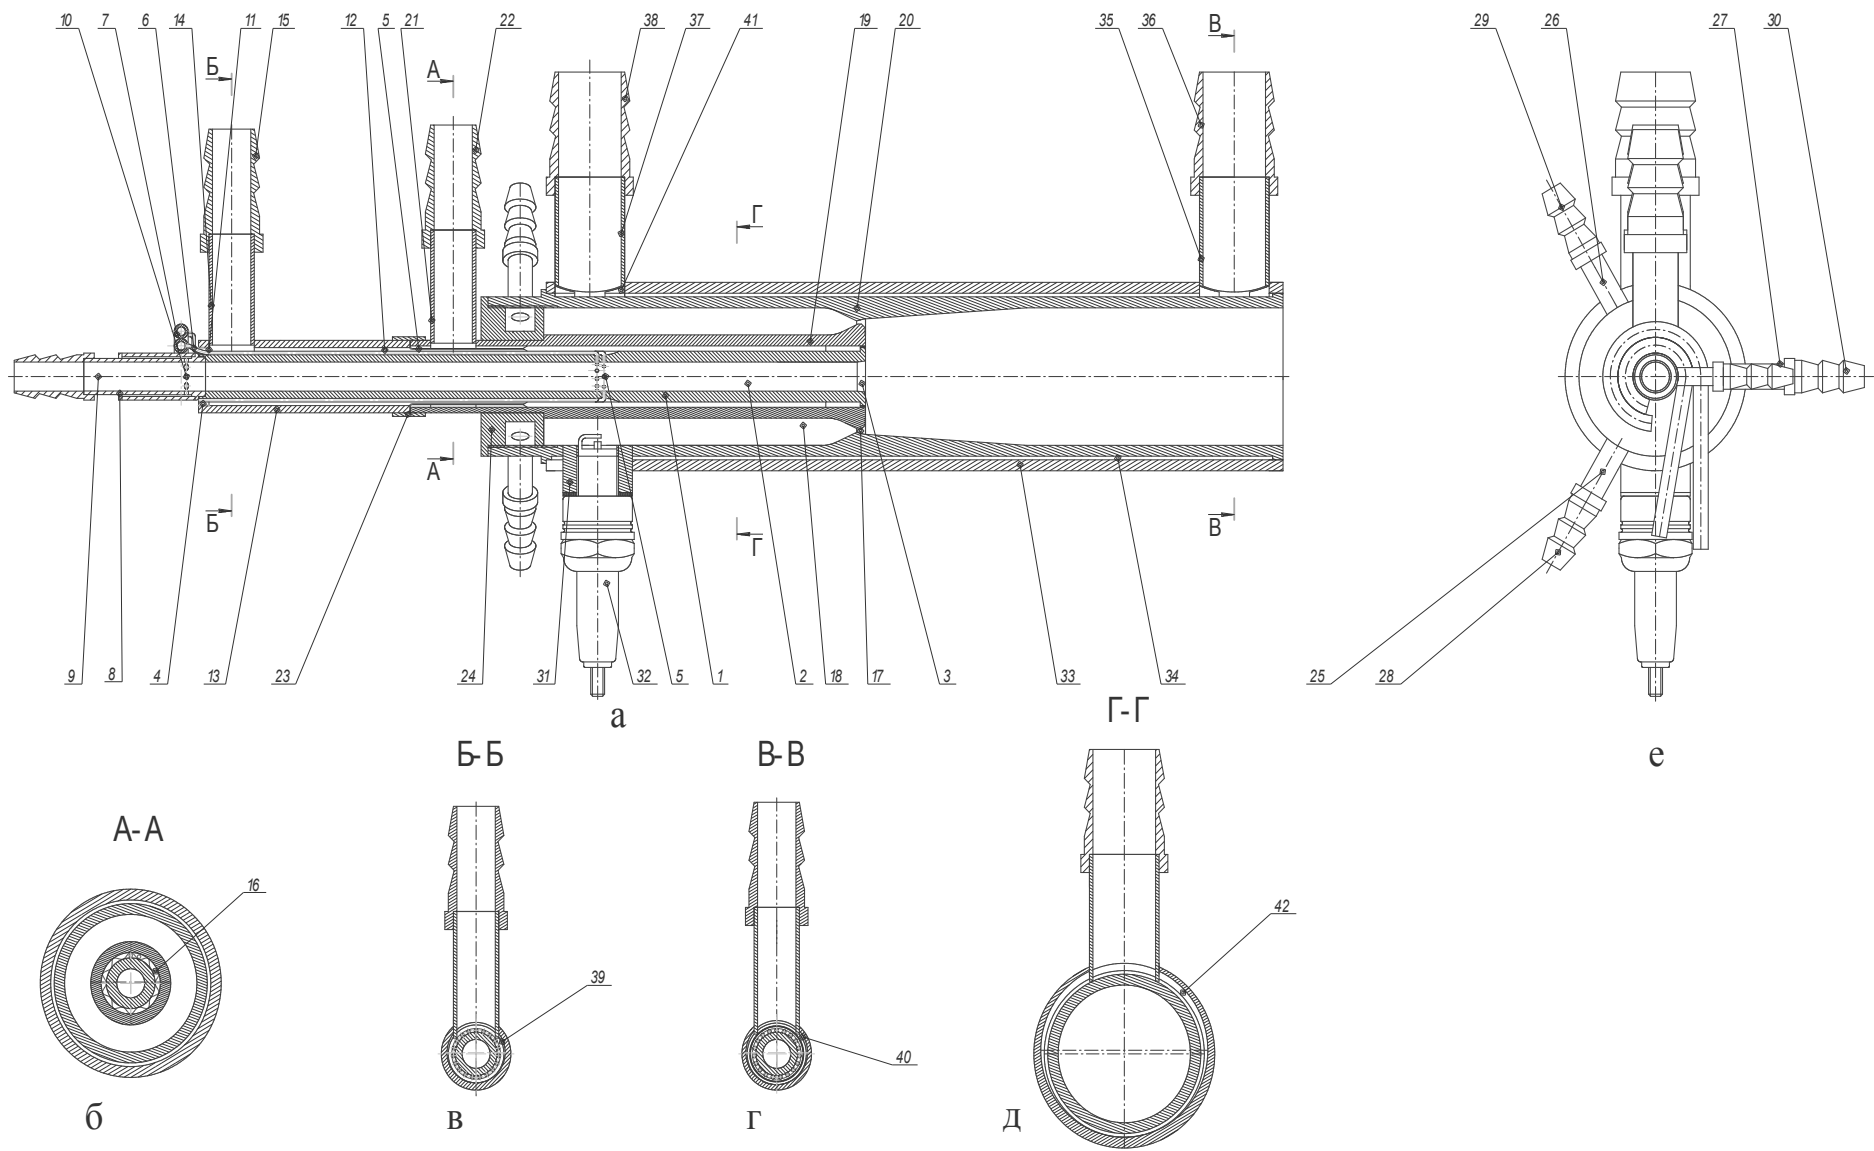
Компоночная схема газопламенной горелки для сверхзвукового напыления покрытий
